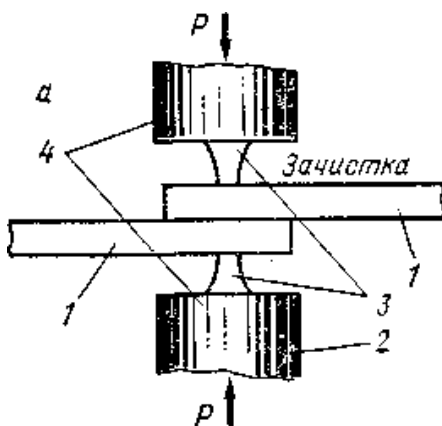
Схема точкового холодного зварювання: 1 — зварювані деталі; 2 – пуанسونи, 3 – виступи на пуансонах; 4 – опорні поверхні пуансонів
